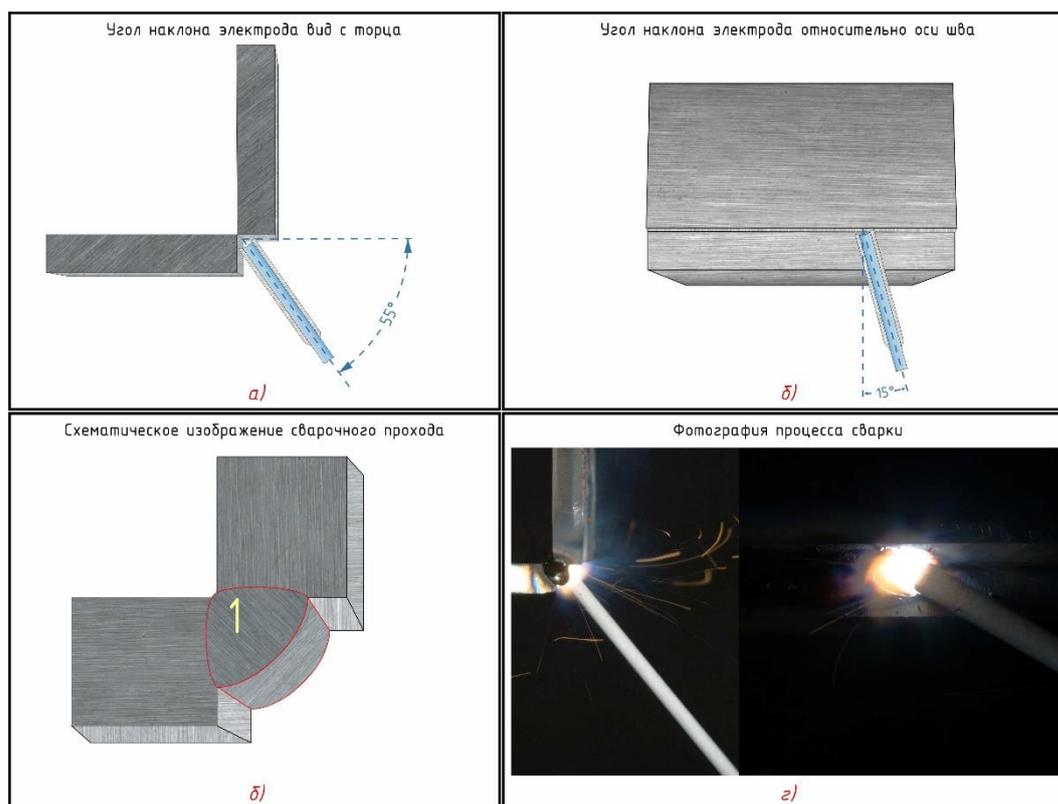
Положение электрода при сварке корневого прохода
